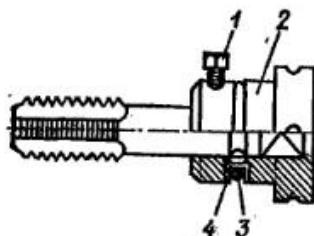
Переходная втулка для крепления метчика в резьбонарезном патроне (см. рис. 80).
